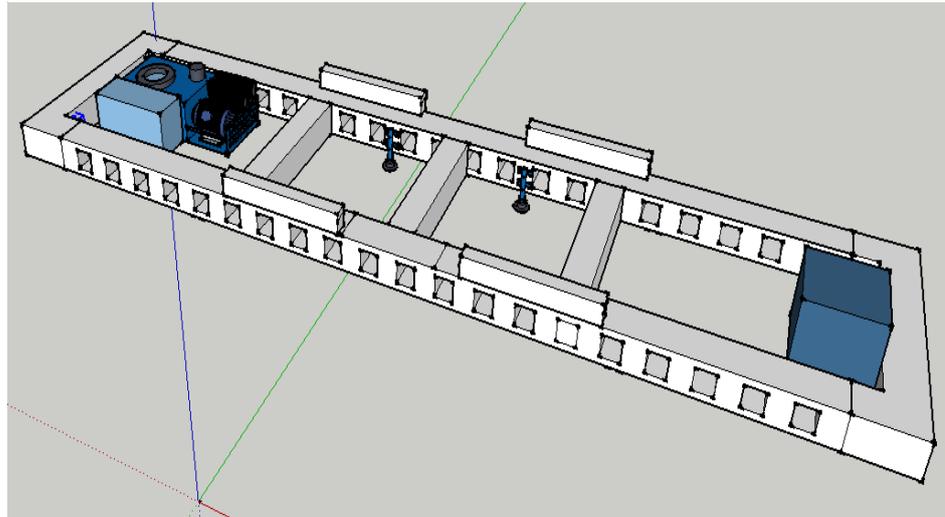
Vista isométrica de las carrileras para los rodamientos
